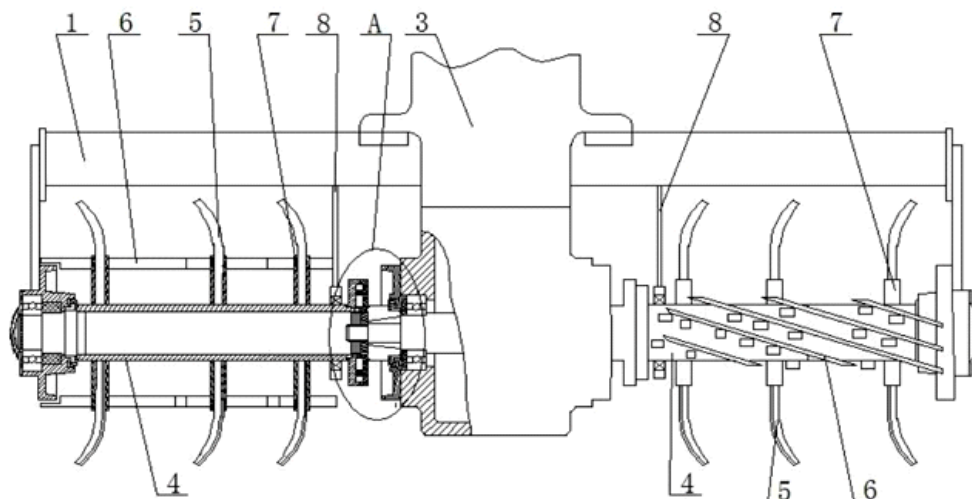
Почвообрабатывающая фреза с устройством защиты от поломок.
